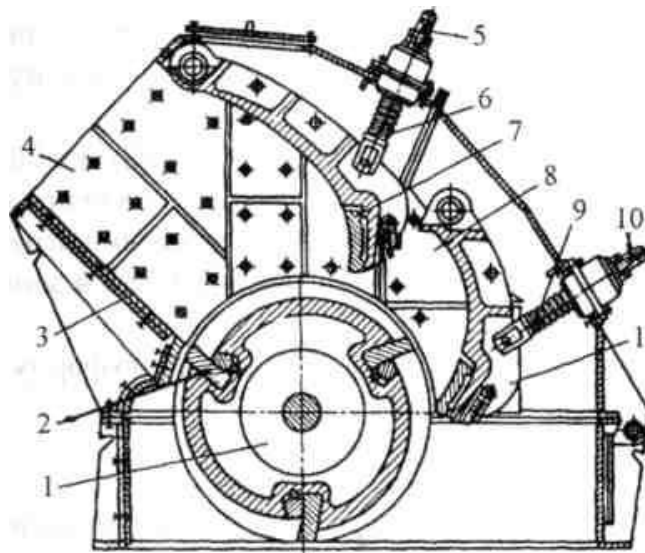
Конструкція однороторної дробарки СМД-85:
